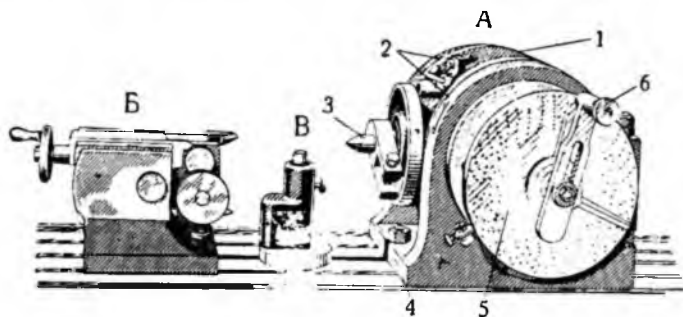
Делительная головка, установленная на рабочем столе универсально-фрезерного станка:
